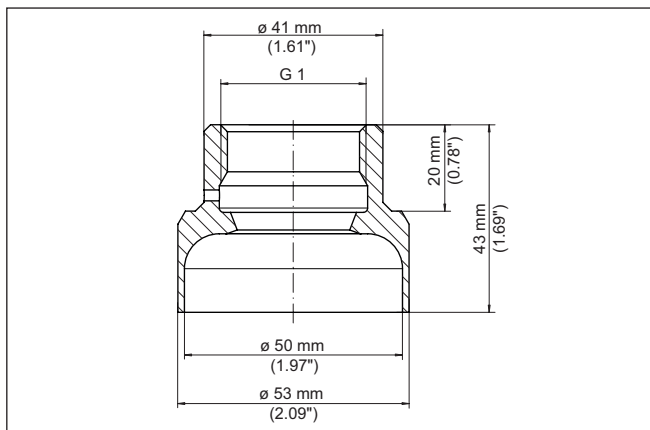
Dimensions raccord à souder direct pour montage sur tube G1 - Joint conique
